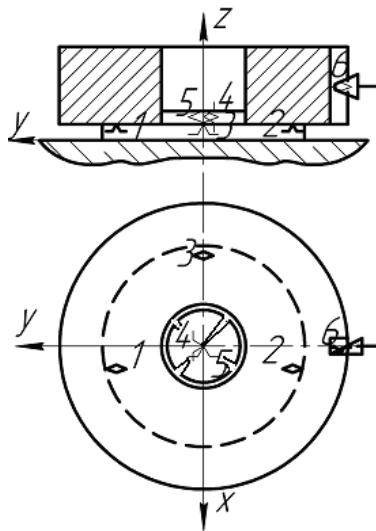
Встановлення диска на п'яту та короткий палець.
